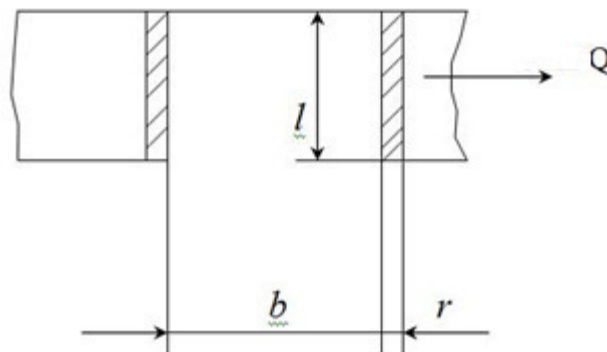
Схема к расчету сварного соединения
